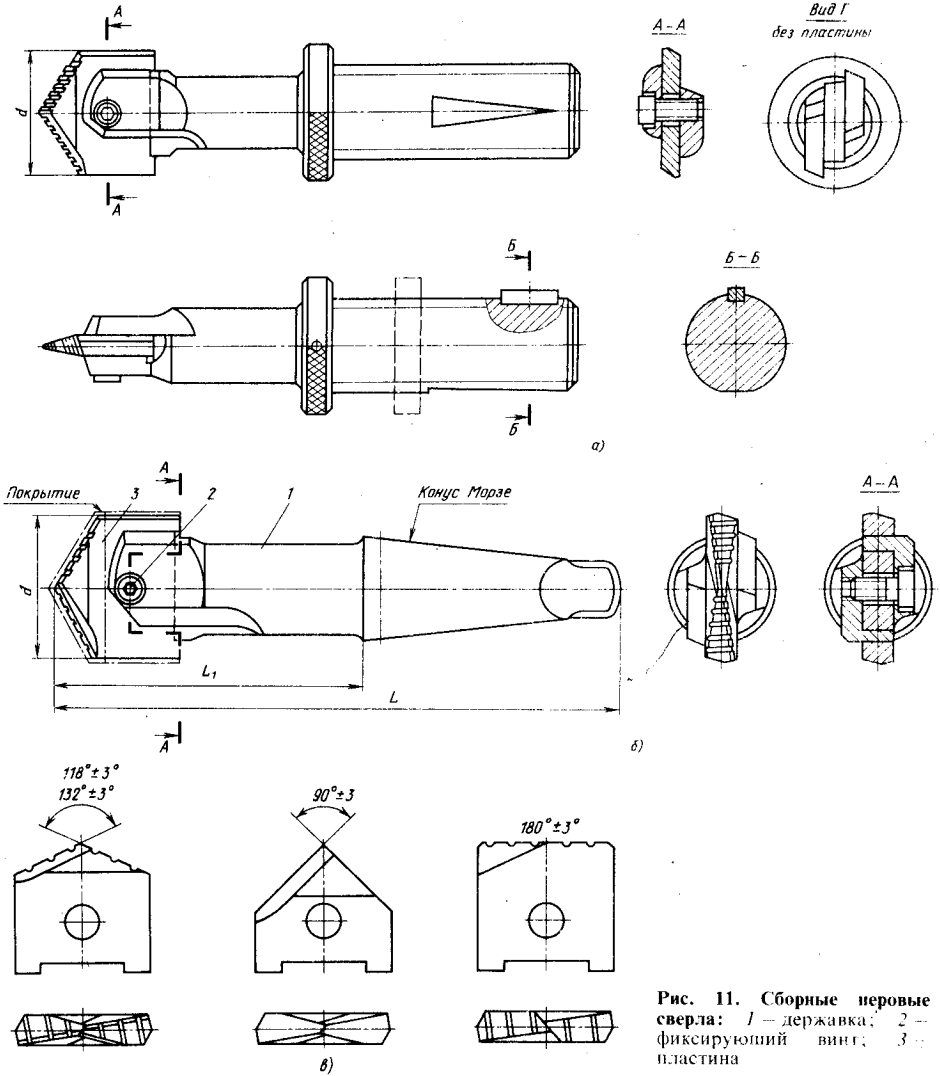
Сборные перовые сверла: 1 — державка; 2 — фиксирующий винт; 3 — пластина
